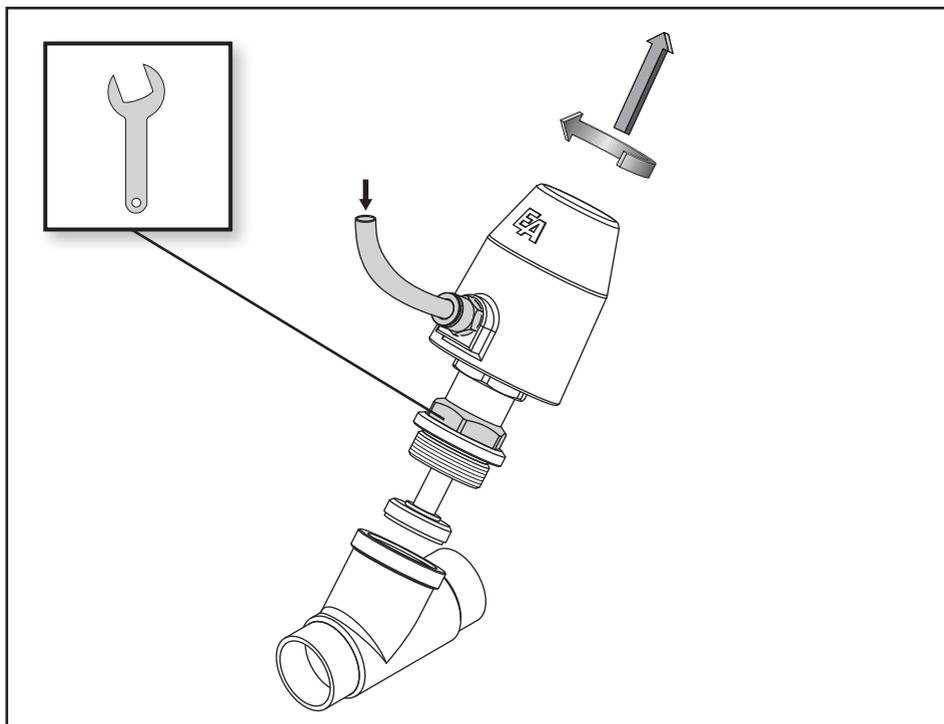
Montage / Demontage - Anschweißenden, demontieren des Ventiloberteils
